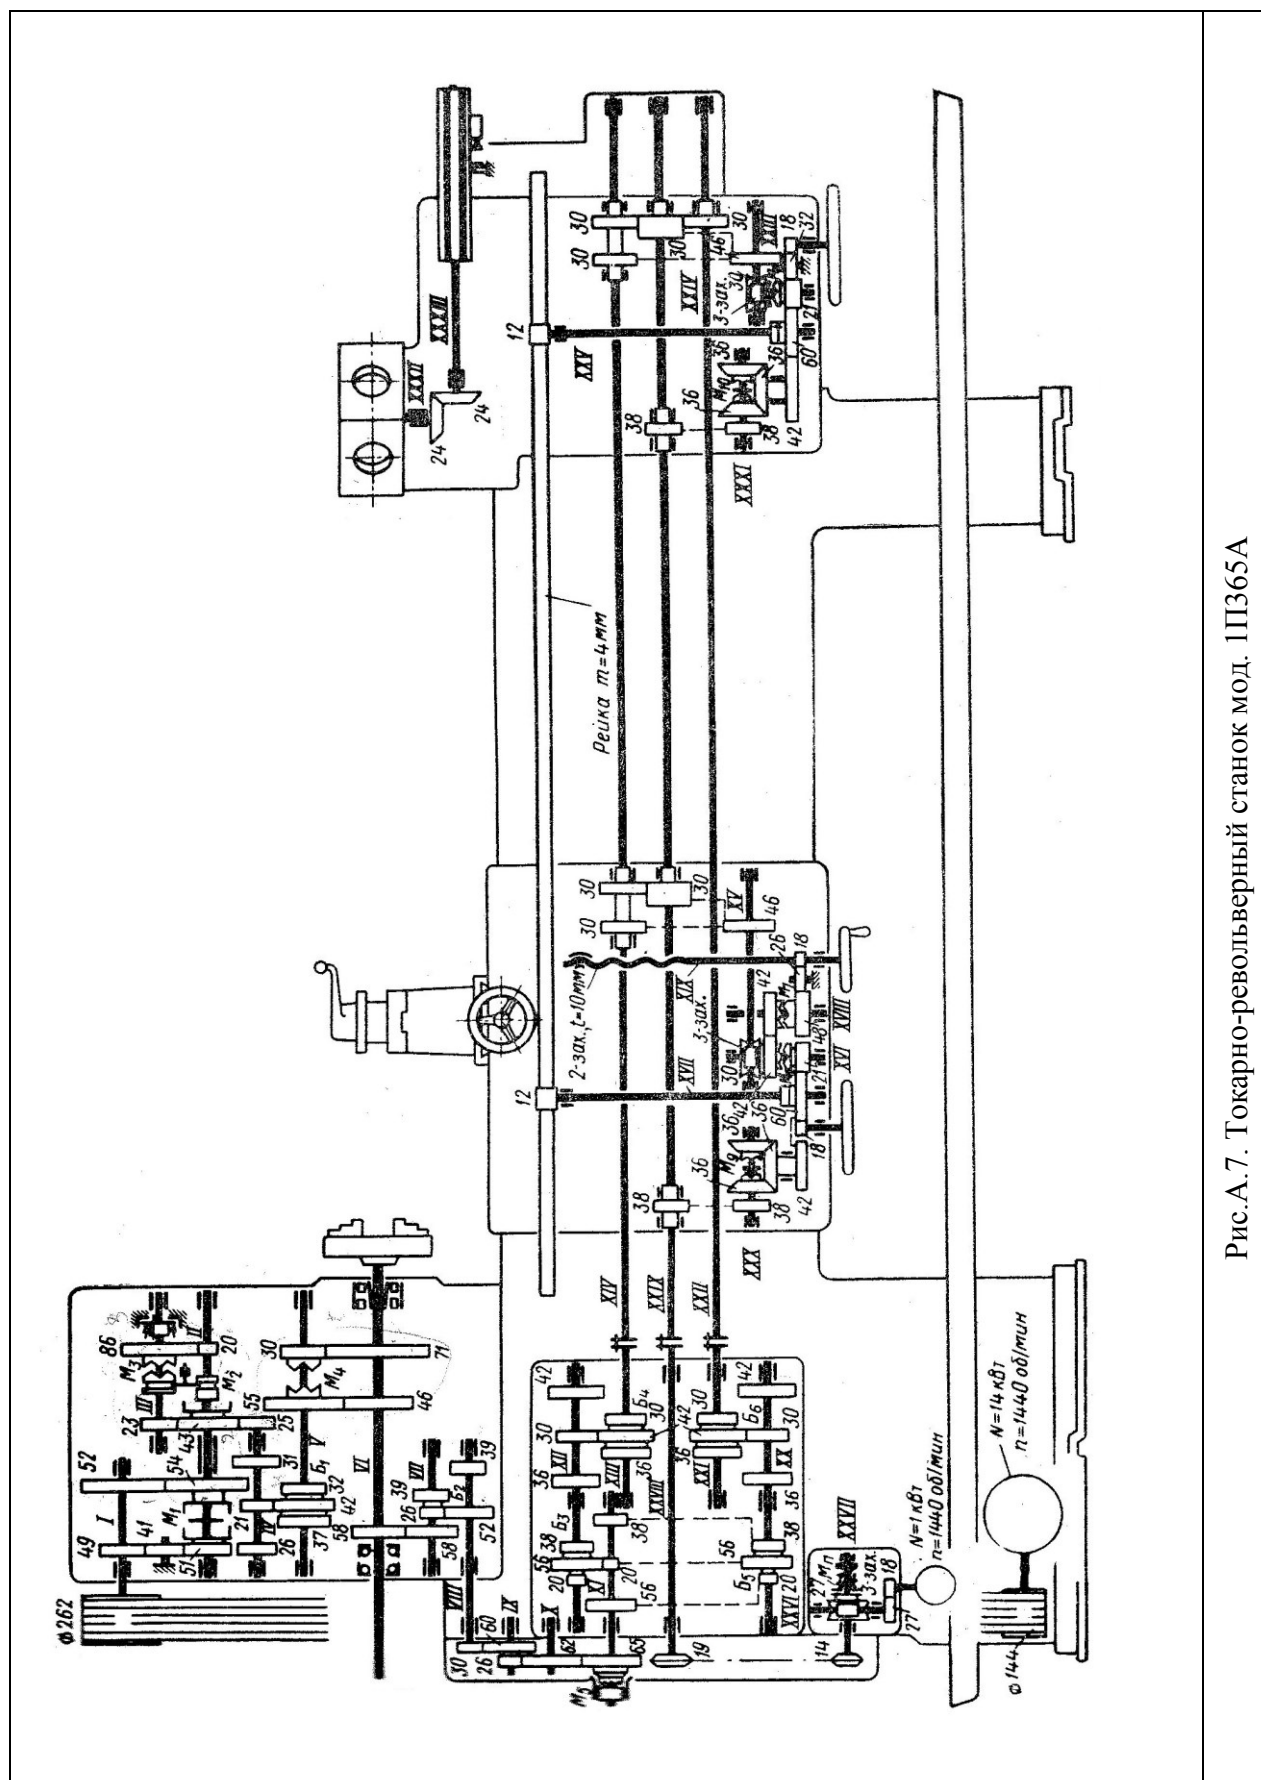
Токарно-револьверный станок мод. 1П365А
